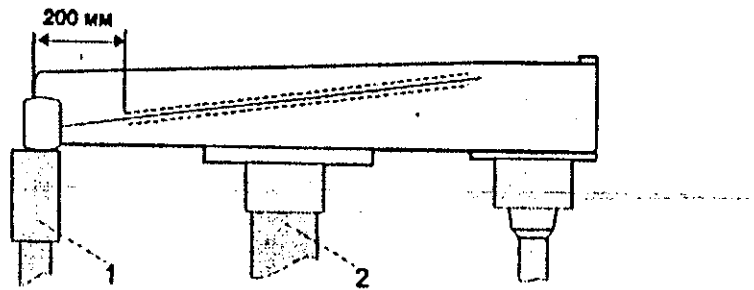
Контроль сварного шва накладок верхнего пояса продольной балки рамы
